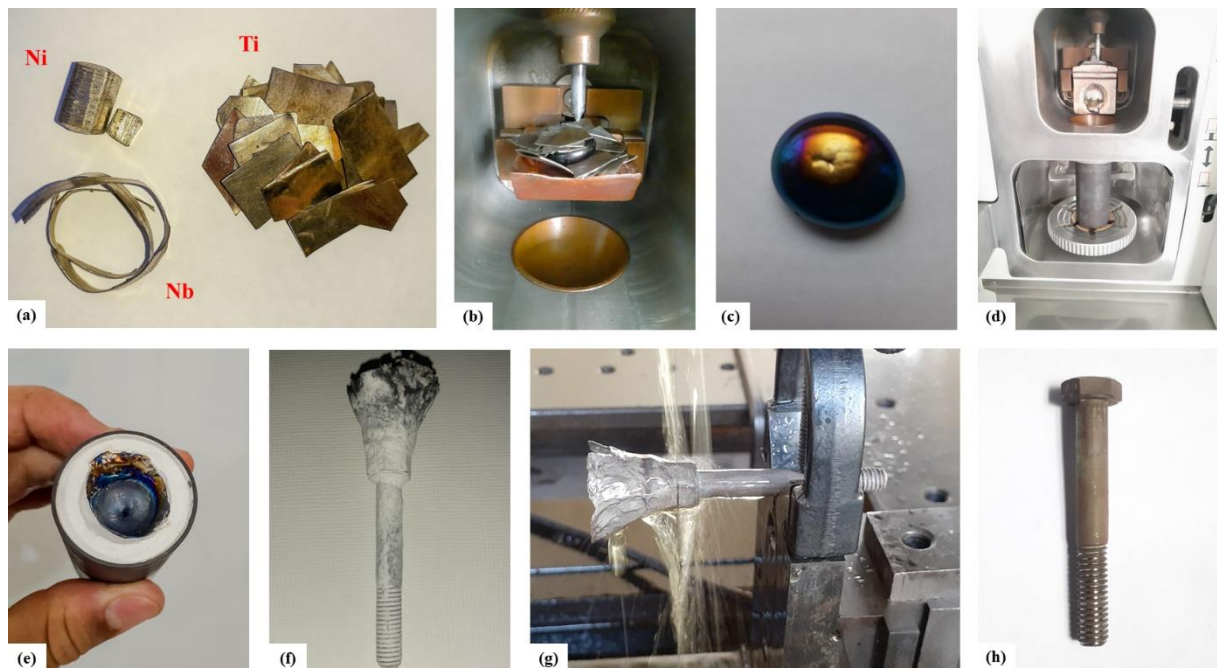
Processo de fabricação dos protótipos de parafusos. (a) Carga de fundição. (b) Câmara de fusão. (c) Botão da liga fundida. (d) Câmaras de fusão e vácuo. (e) Molde injetado. (f) Produto fundido. (g) Corte por eletroerosão a fio. (h) Produto acabado. Autoria Própria.
